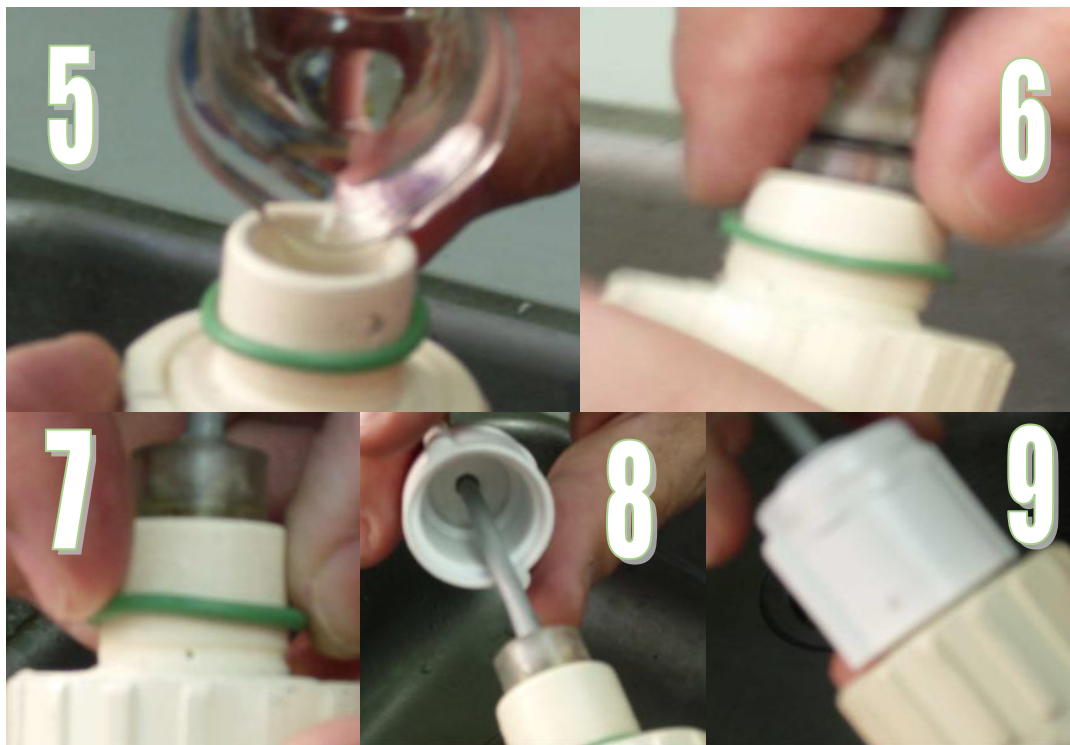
Ensamble del Sensor Voltamétrico de Hidrógeno, segunda parte
